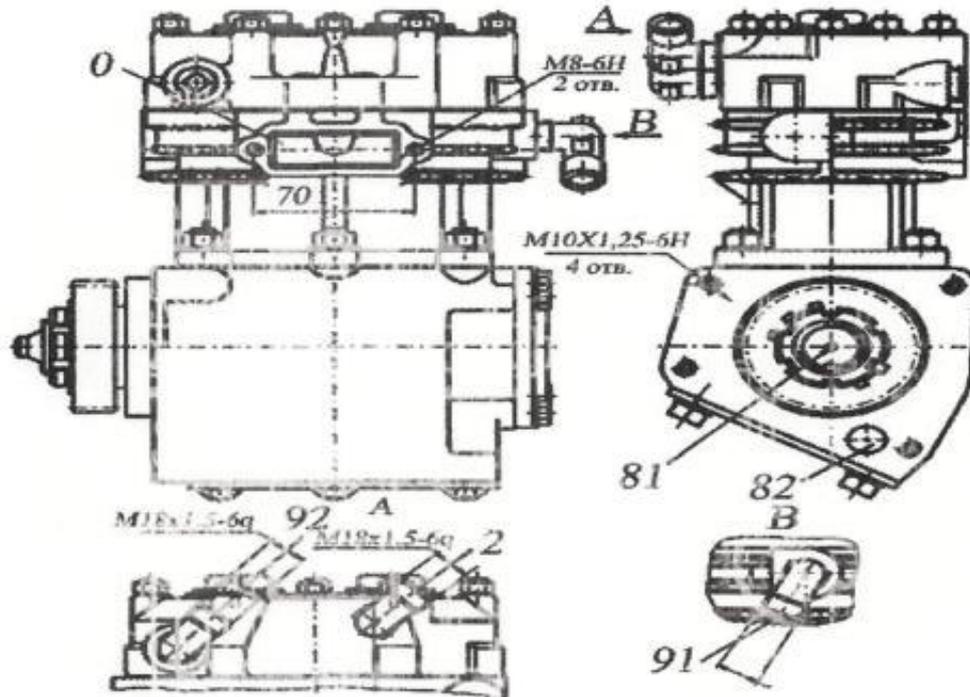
Схема компрессора KaMA3 5320-3509015
